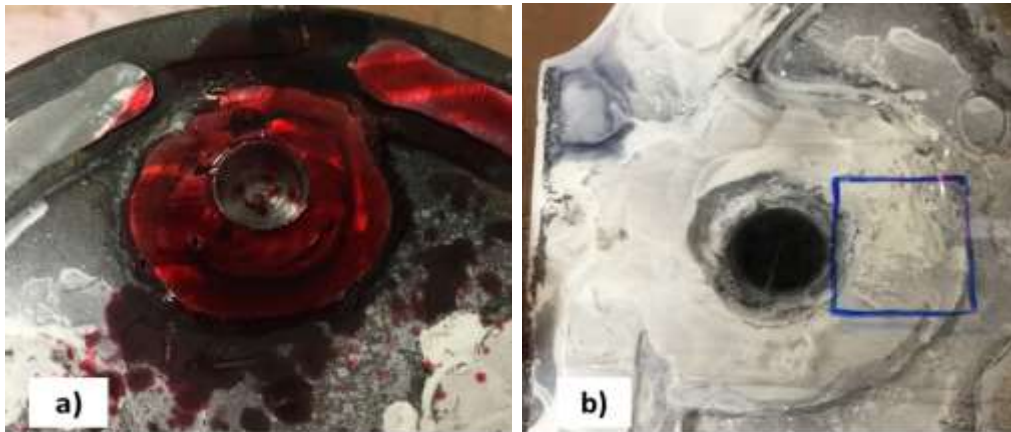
3 a) Aplicación de líquido penetrante sobre zona soldada, b) Aplicación de líquido revelador para observar discontinuidades presentes en soldadura
